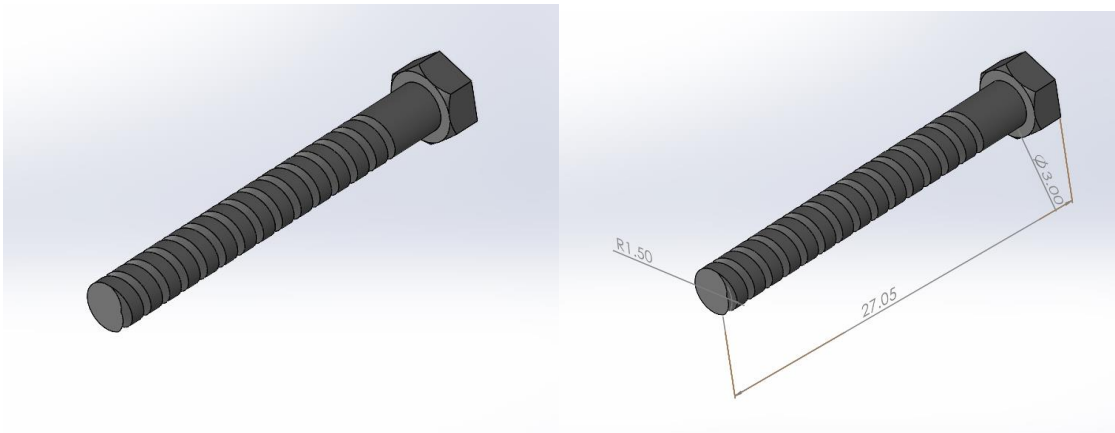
Tornillo sin fin milimétrico. Fuente: propia.
